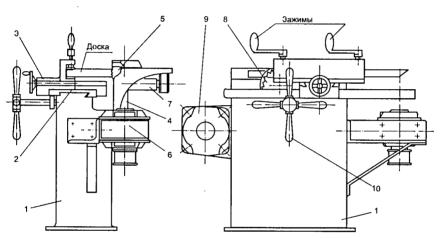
Общий вид станка для изготовления клиньев: 1 — литая станина, 2 — салазки горизонтального хода, 3 — салазки поперечного хода, 4 — вал фасонной фрезы, 5 — фасонная фреза, 6 и 9 — электродвигатель, 7 — вал дисковой пилы, 8 — дисковая пила, 10 — штурвал
